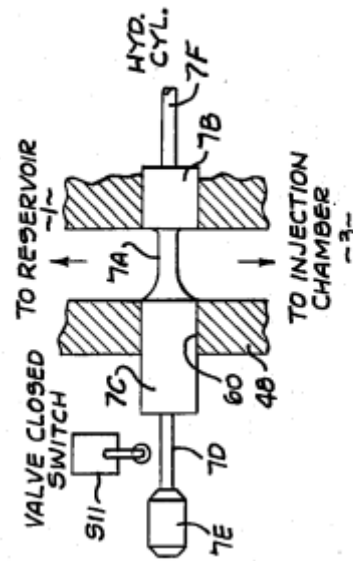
поздовжній вид золотникового клапана, який використовується в вузлі сопла для керування потоком парафіну між резервуаром і камерою впорскування воску
